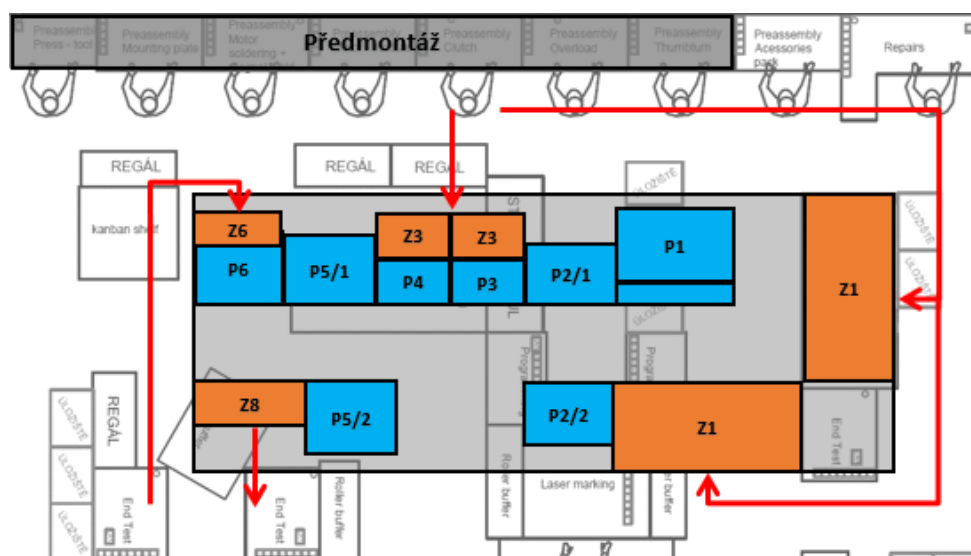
Návrh layoutu-varianta B (Zdroj: Vlastní zpracování)
